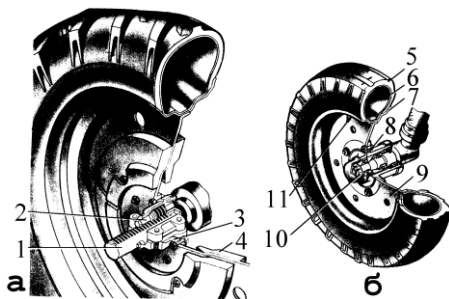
Колеса пропашного трактора: а – ведущее (трактор МТЗ-80); б – направляющее (трактор МТЗ-80); 1 – полуось; 2 – червяк; 3 – вкладыш; 4 – груз; 5 – покрышка; 6 – камера; 7 – обод; 8 – ступица; 9 – диск; 10 – регулировочная гайка; 11 – вентиль
